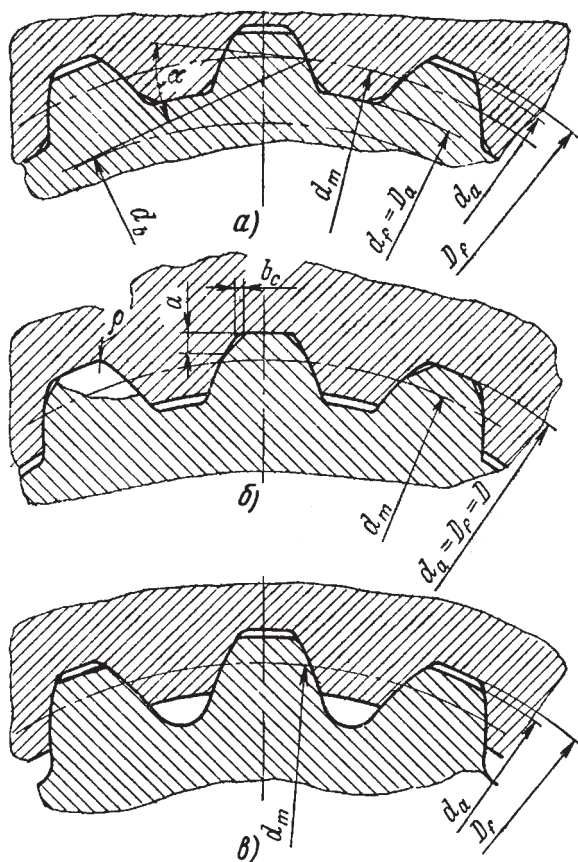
Центрирование шлицевого соединения с эвольвентными зубьями:
